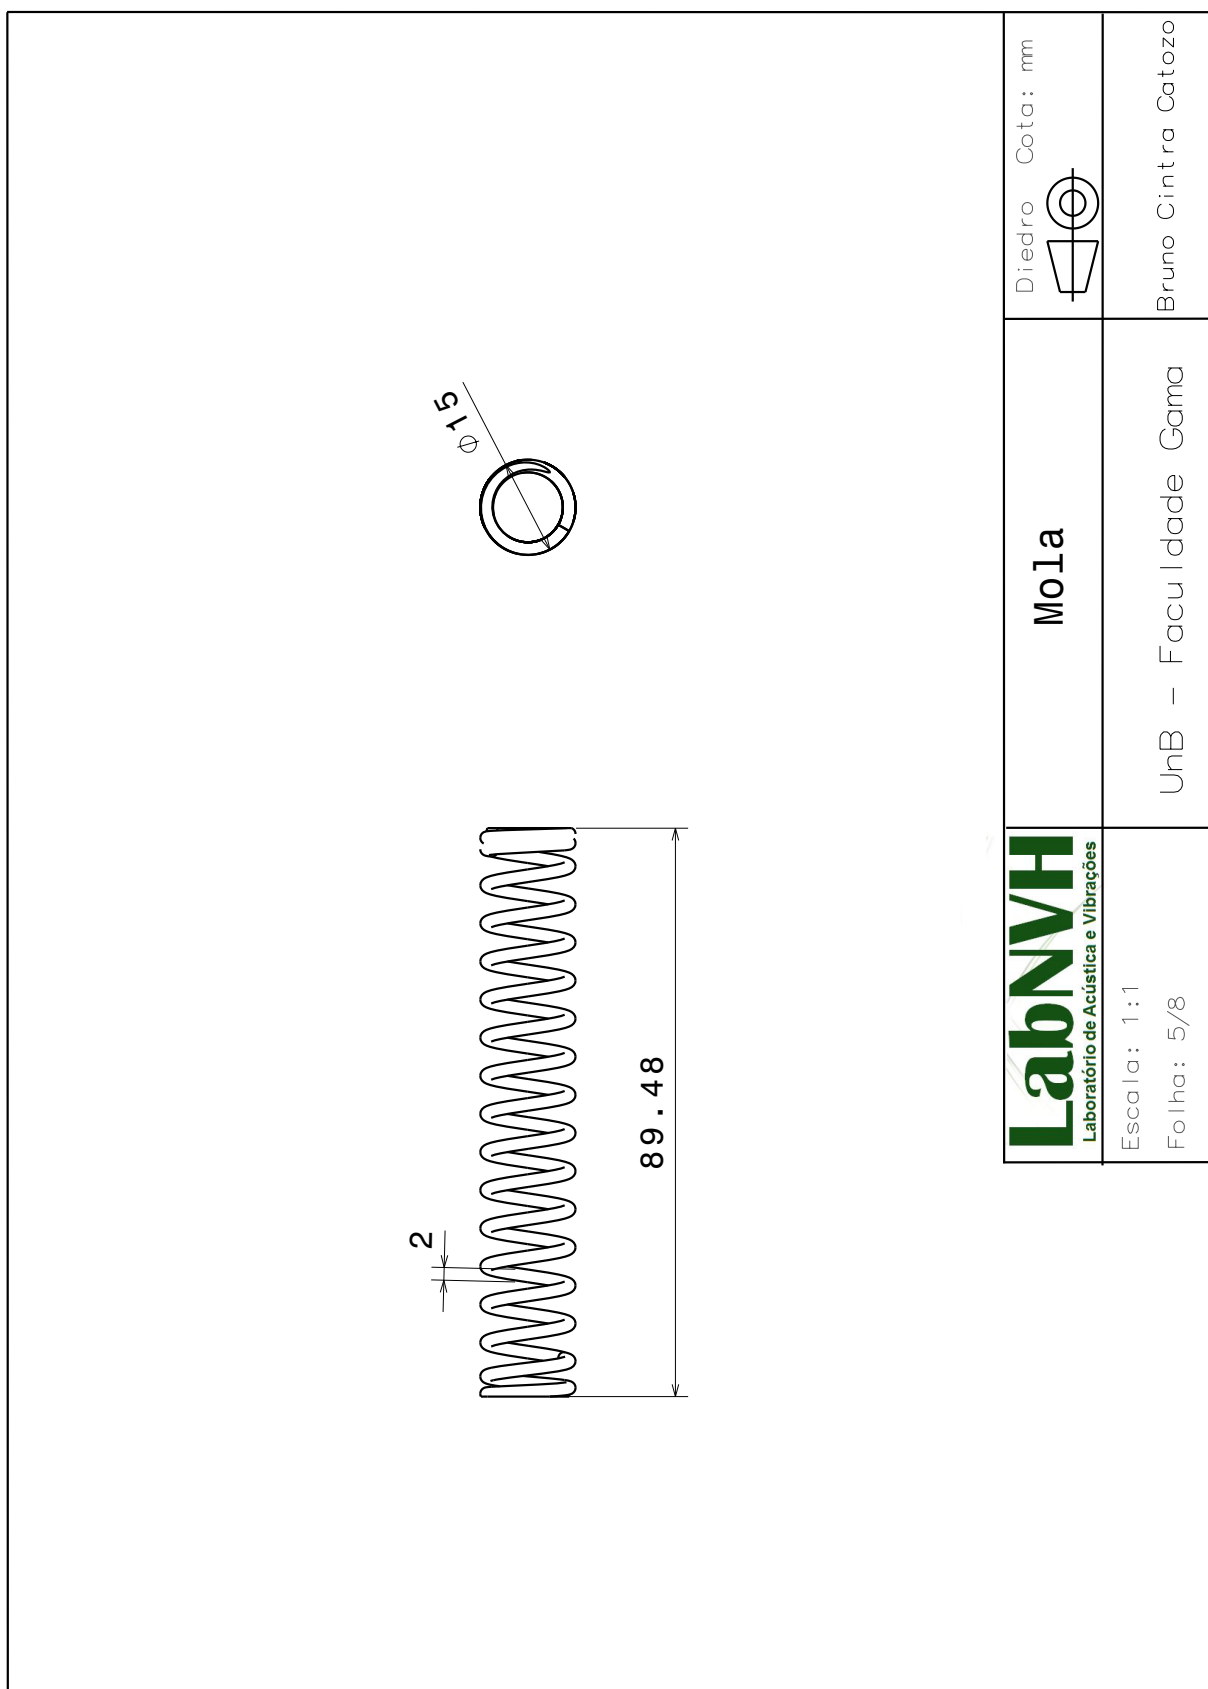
Desenho técnico da mola de aço SAE 1070.
